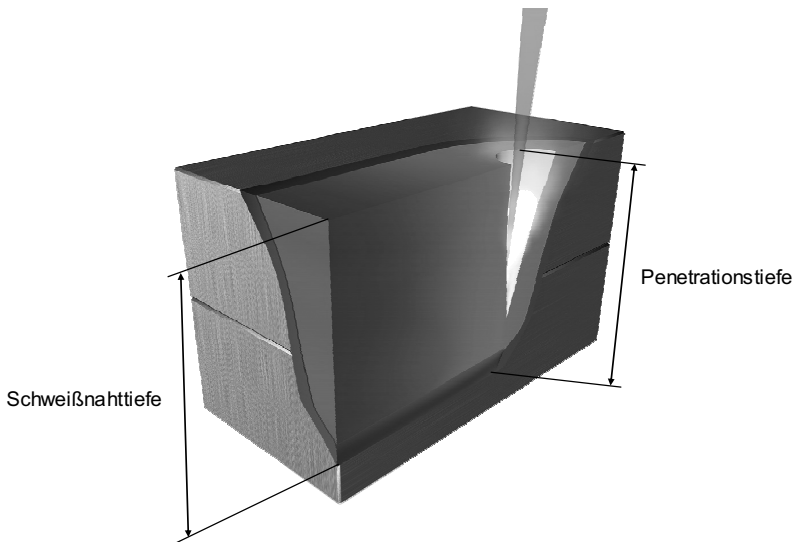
Penetrations- und Schweißnahttiefe beim Laserstrahlschweißen
